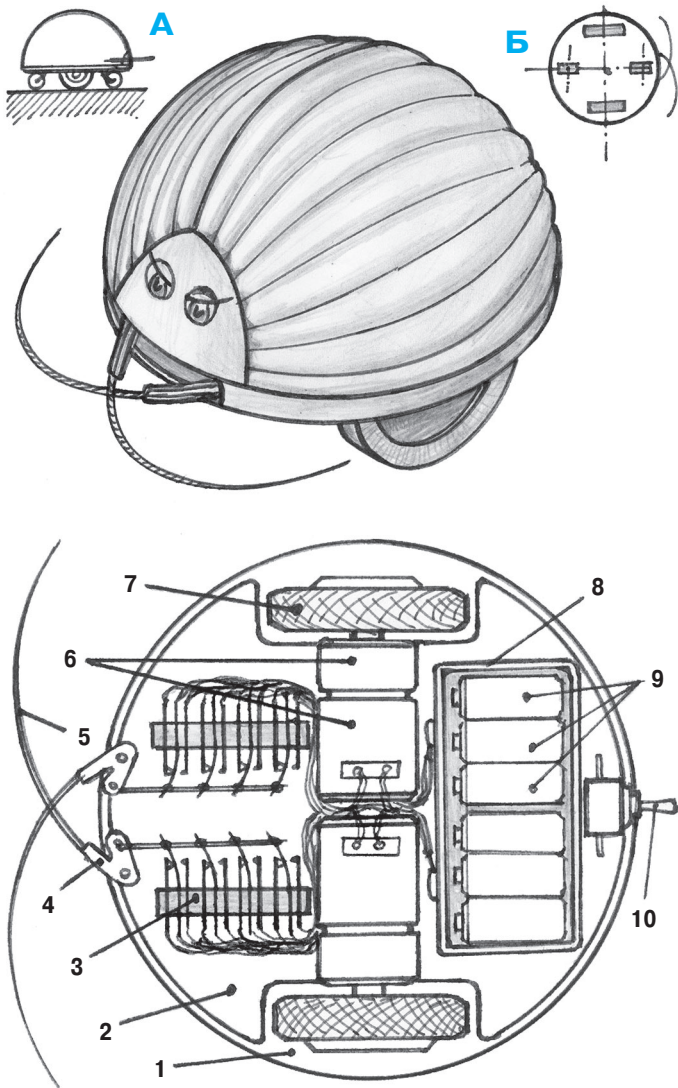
Компонка модели: 1 — корпус; 2 — монтажная плата; 3 — контактная группа; 4 — рычаг усика; 5 — упругая часть усика; 6 — электродвигатель с редуктором; 7 — ведущее колесо; 8 — контейнер для батарей питания; 9 — батареи питания; 10 — выключатель.
